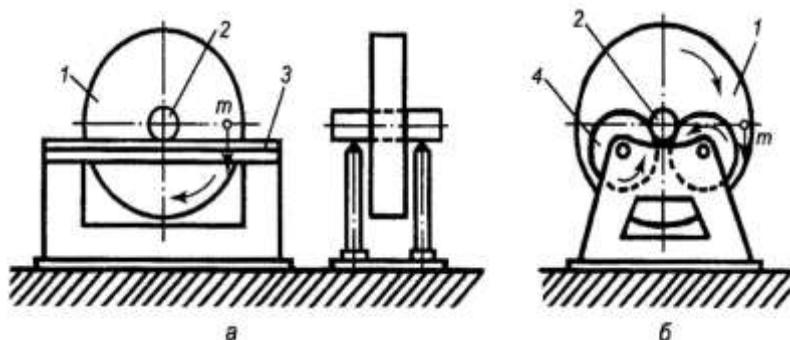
Схемы устройств для статической балансировки с призмами (а) и дисками (б); 1 — балансируемый объект; 2 — оправка; 3 — призма; 4 — диск
